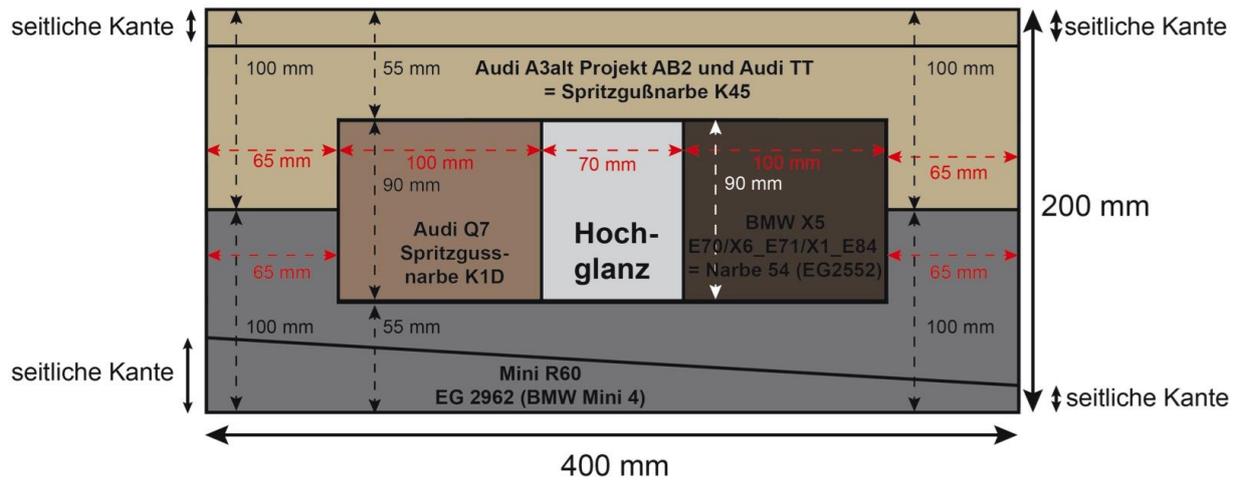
Oberfläche des 2K-Wendeplattenwerkzeugs mit drei Ledernarben, einer technischen Narbe und einer Hochglanzplatte
